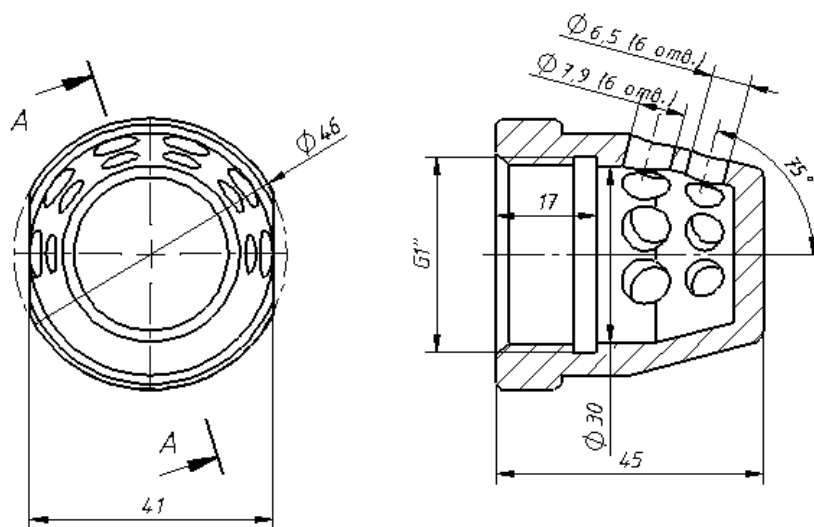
Общий вид распылителя РГ-Л-Н-490-G1"
